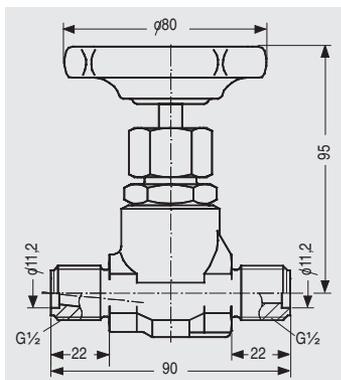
/132 Запорный вентиль 7MF9017-1A, размеры
